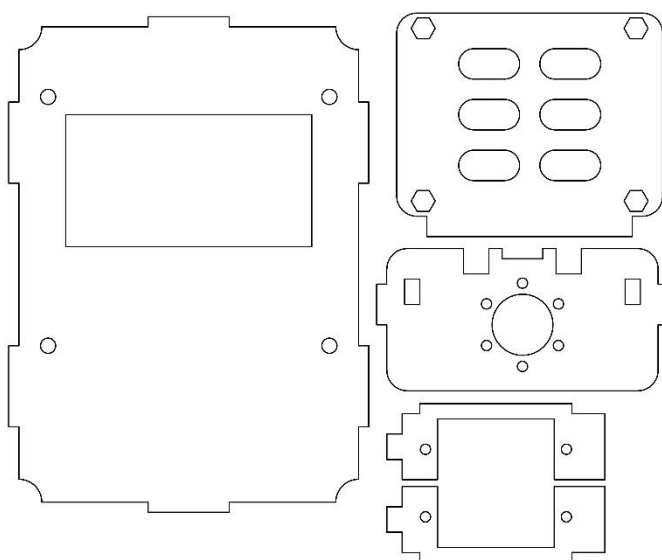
Piezas de la parte superior del robot diseñadas en Inventor
